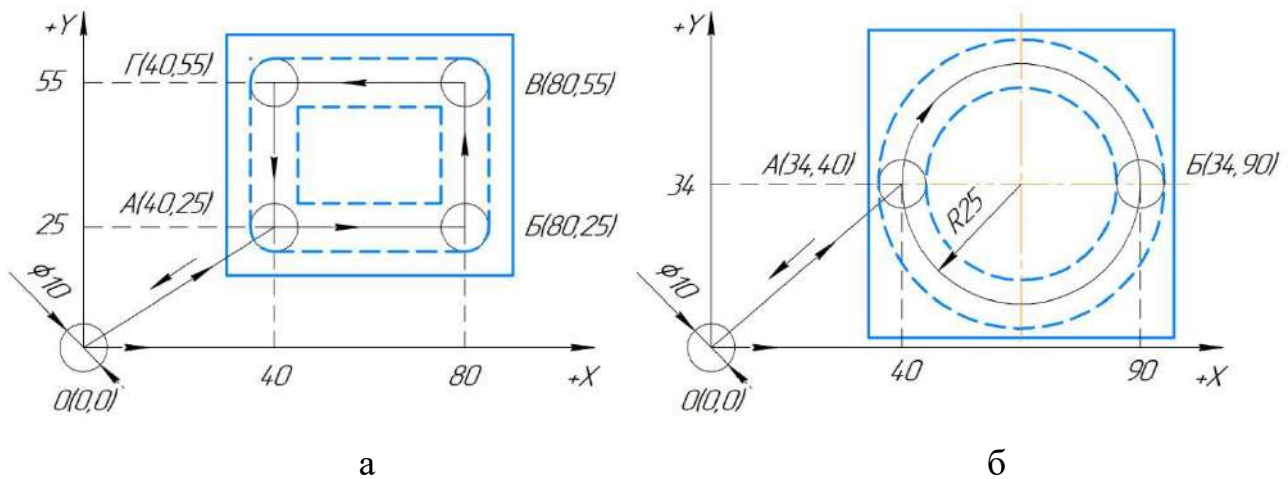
Фрезерування канавки по прямій (а) і по колу (б)
